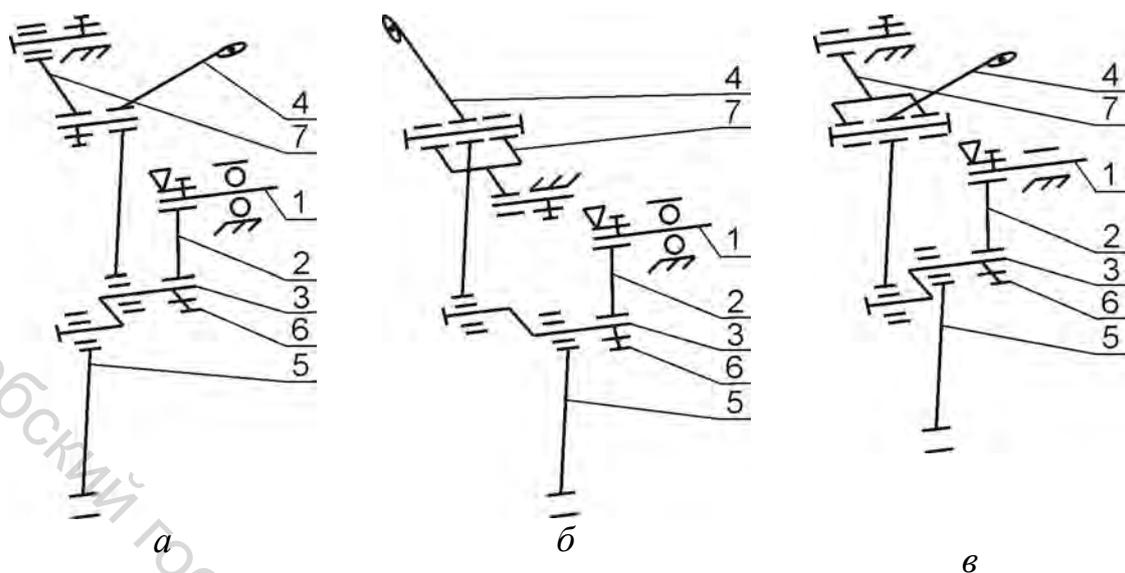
Кинематические схемы механизмов нитепритягивателя:
